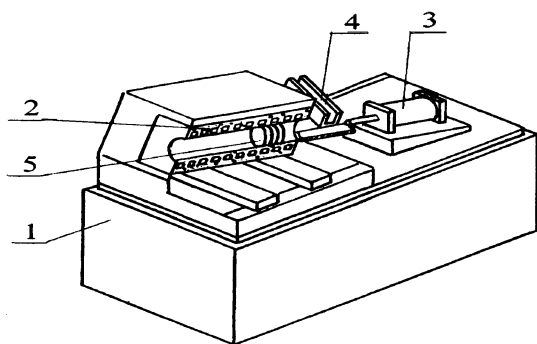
Схема установки для нагрева плоских цилиндрических заготовок диаметром, превышающим длину: 1 — конденсаторный блок; 2 — индуктор; 3 — пневмоцилиндр толкателя; 4 — лоток загрузки; 5 — нагреваемая заготовка
